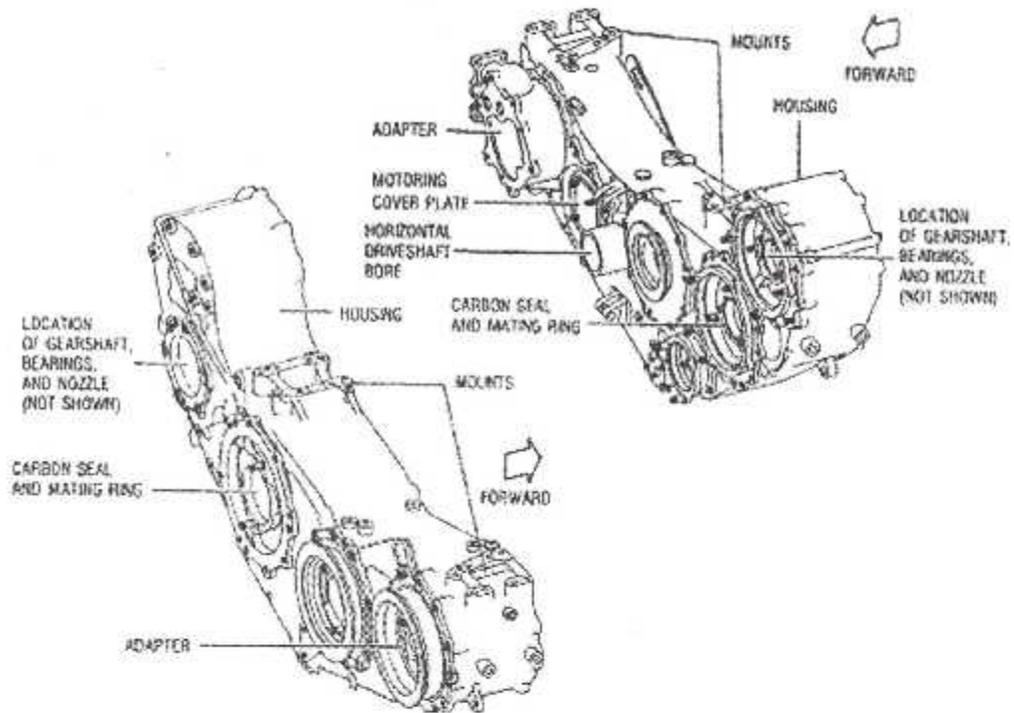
Les différents accessoires entraînés par la gearbox
